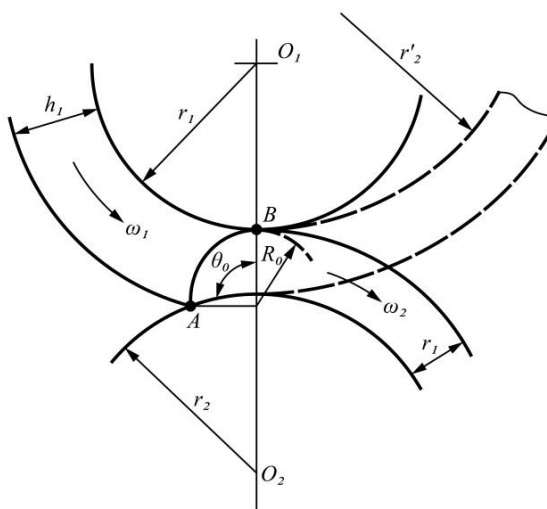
Схема деформации при прокатке с изгибом заготовки
